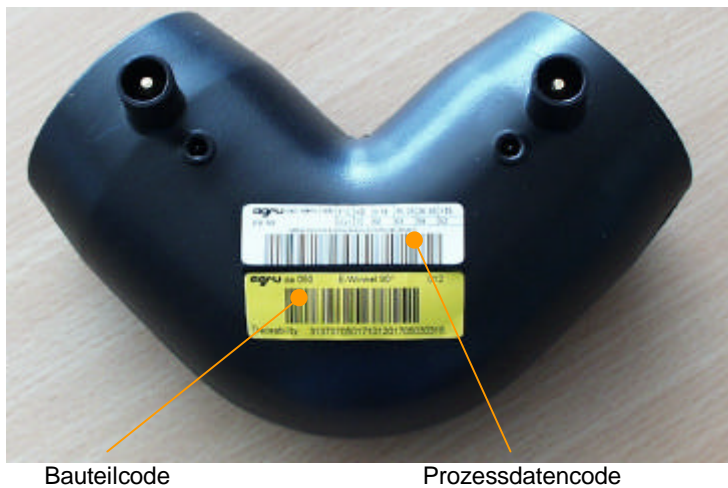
Formteil für HW-Schweißung mit Rückverfolgbarkeitscode
